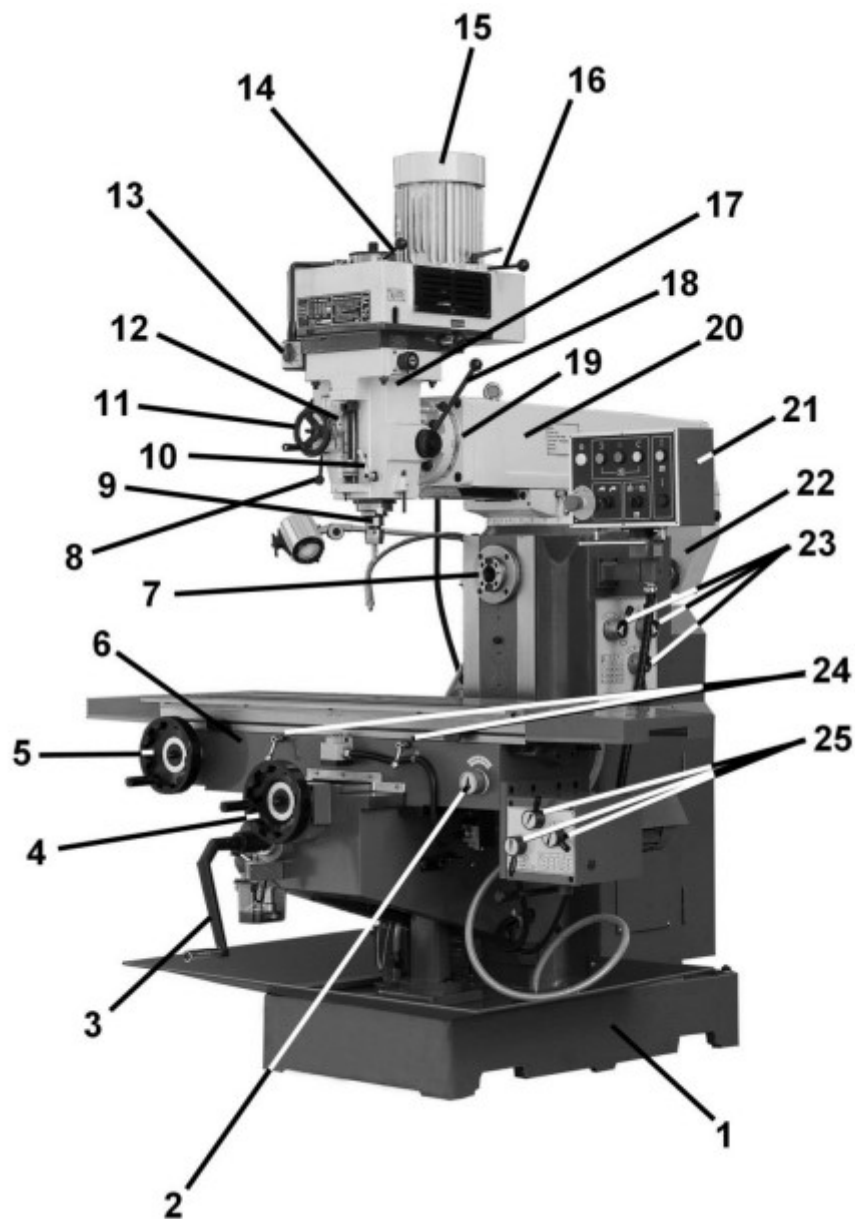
Будова фрезерного верстату TMM 700 Vario FDB Maschinen
